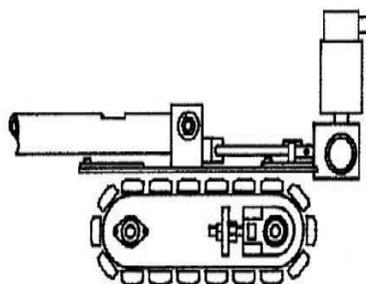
Внешний вид робота с цельной рабочей конструкцией
